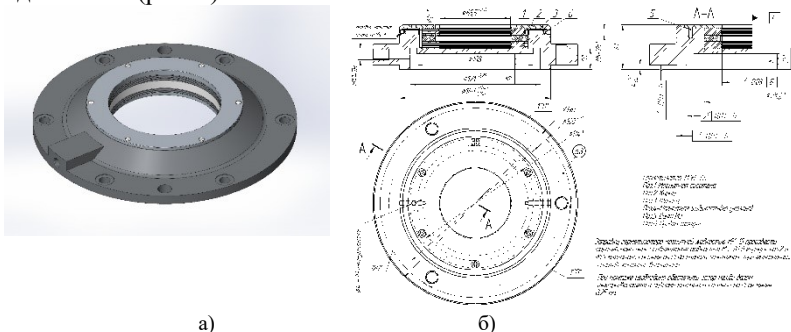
МЖГ (а) и чертеж МЖГ (б) в конструкции крышки подшипника
